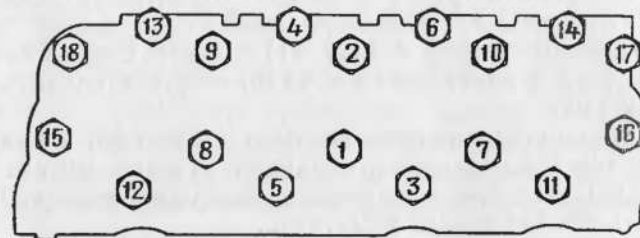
Порядок затяжки гаек головки блока цилиндров
